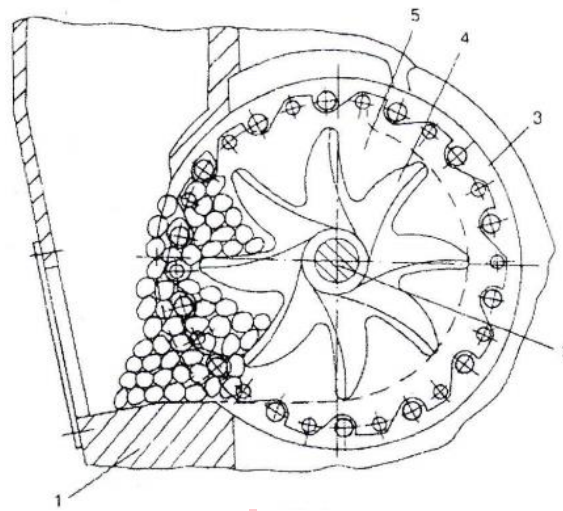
Пневматичний висівний апарат: 1 - корпус; 2 - вал; 3 - висівний диск; 4 - ворушилка; 5 - вирізний диск
